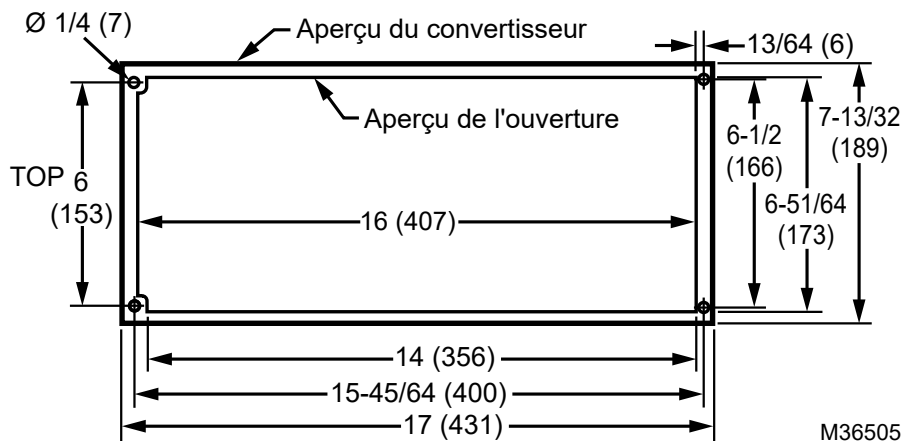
Schéma des dimensions en montage par bride, pour MI5 [unité : pouces (mm)]
